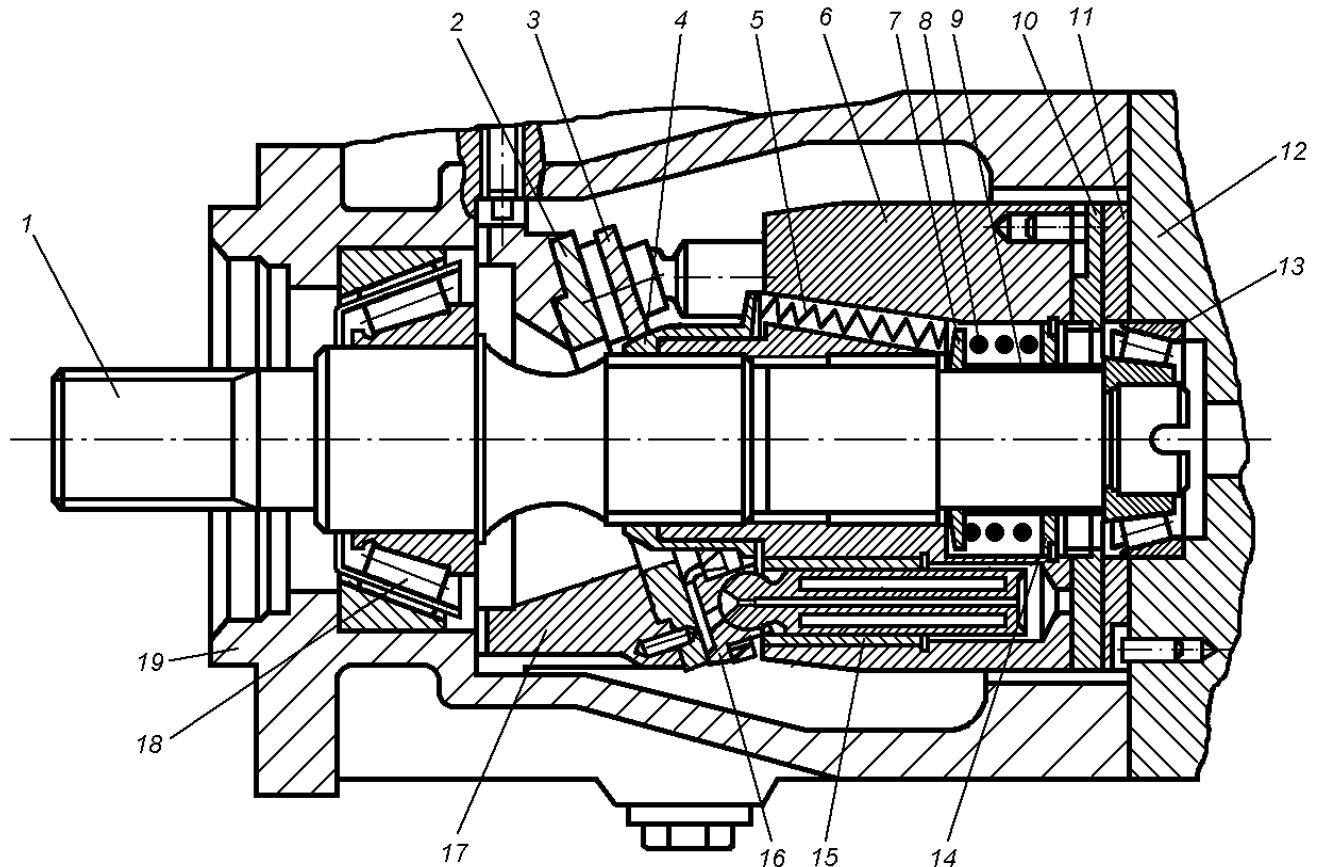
Реверсивный нерегулируемый аксиально-поршневой гидромотор МП-90:
